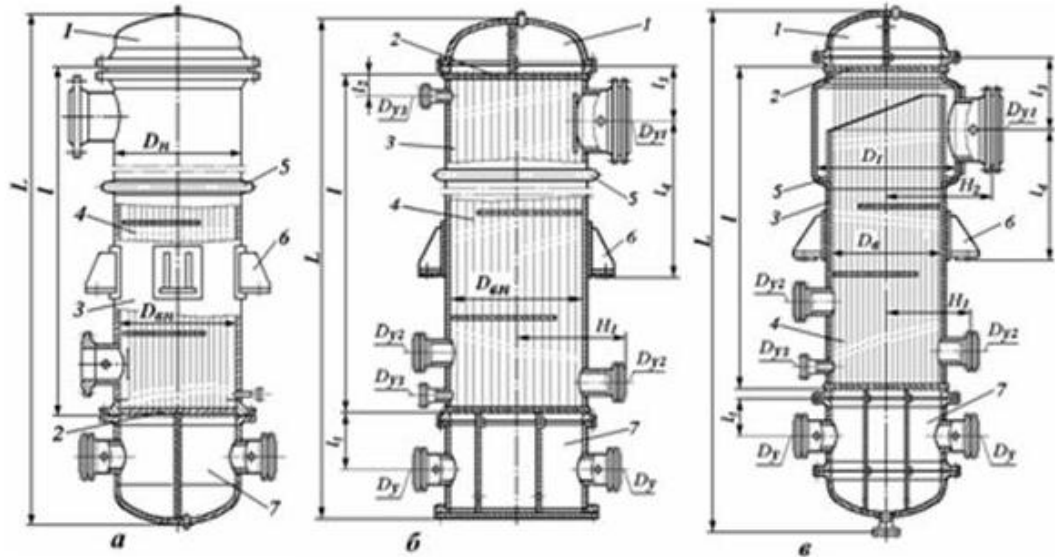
Кожухотрубні конденсатори вертикальні напівжорсткого типу: а - з нероз'ємною розподільною камерою; б - з роз'ємною камерою і плоским днищем; в - з роз'ємною камерою і двома еліптичними кришками; 1 - кришка; 2 - трубна решітка; 3 - корпус-кожух; 4 - трубчатка; 5 - температурний компенсатор; 6 - опора; 7 - камера розподільна.
